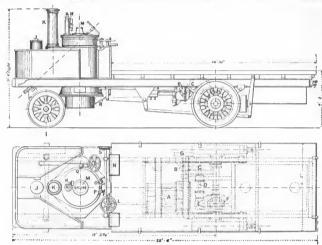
und 5. Aufriss und Grundriss des Thornycroft 7 t-Lastwagen.
